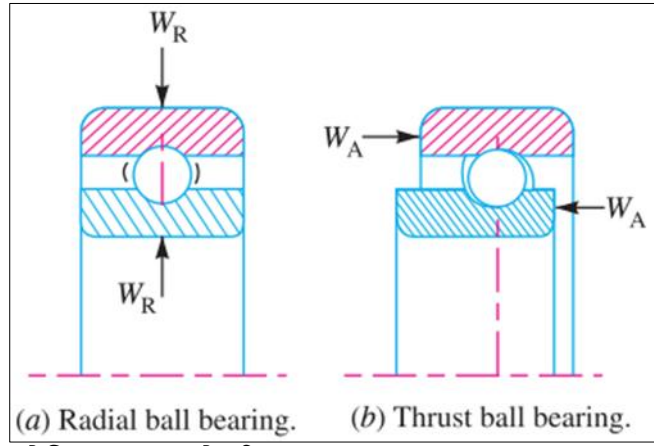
रेडियल व थ्रस्ट बेअरिंग्स (Radial and Thrust Ball Bearings)
